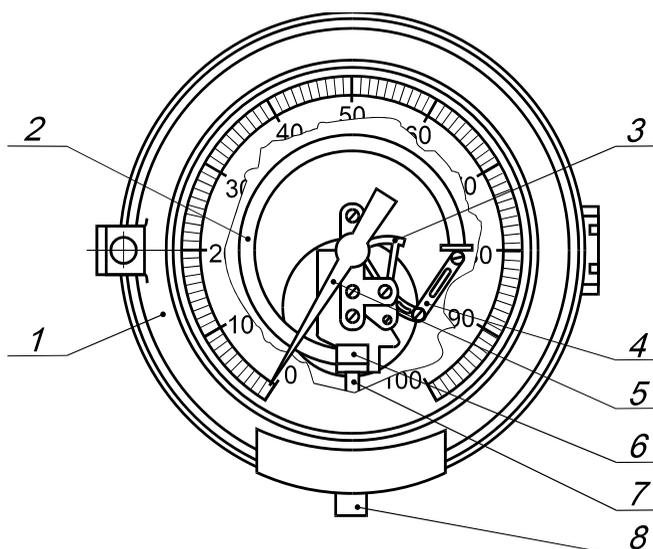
Манометрический механизм указателя с основной шкалой:
